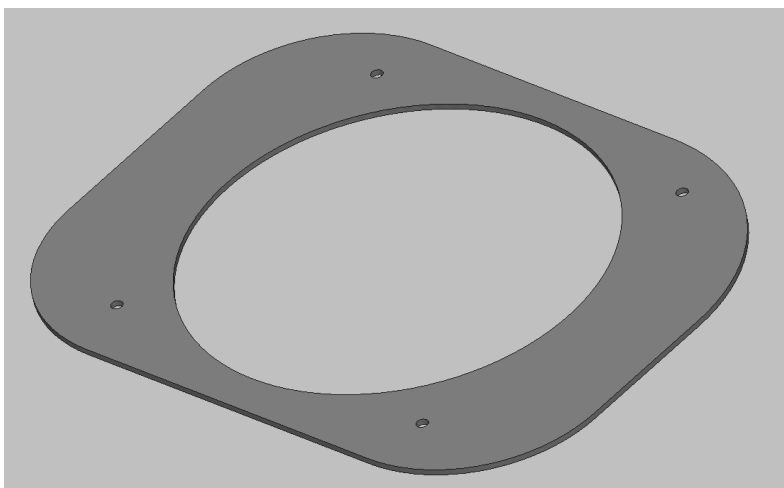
3D-модель детали для крепления корпусного вентилятора
